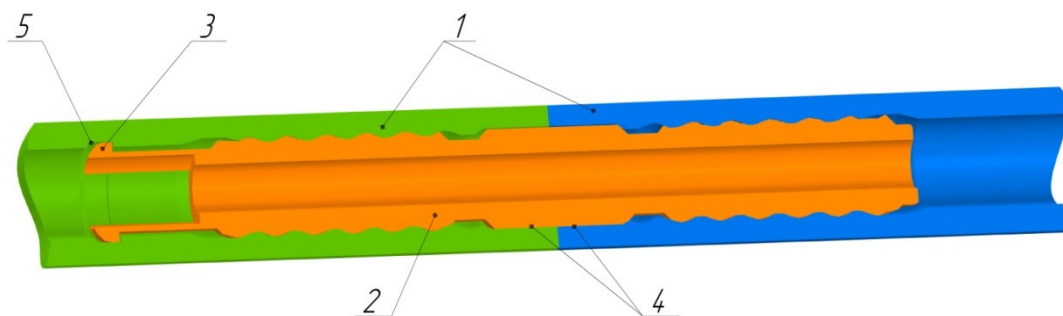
Ниппельное соединение с резьбой круглого профиля
